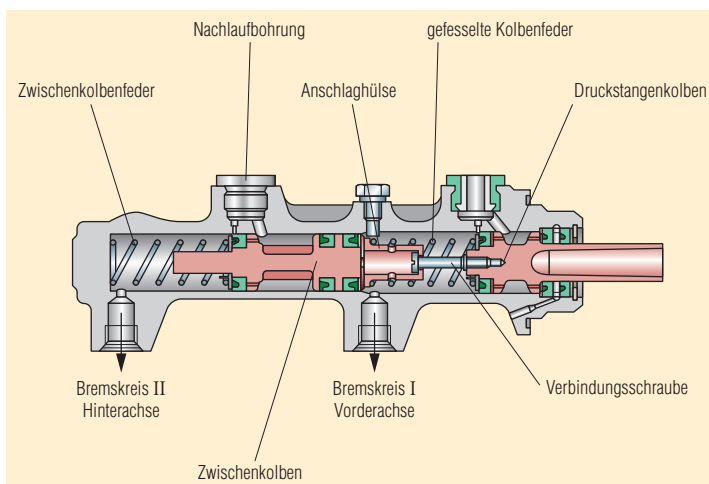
Tandem-Hauptzylinder mit gefesselter Kolbenfeder.
